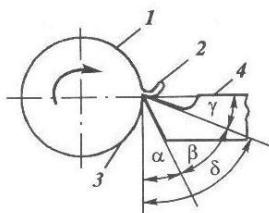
Схема процесса резания на токарном станке: 1 – обрабатываемая поверхность; 2 – стружка; 3 – обработанная поверхность; 4 – резец
